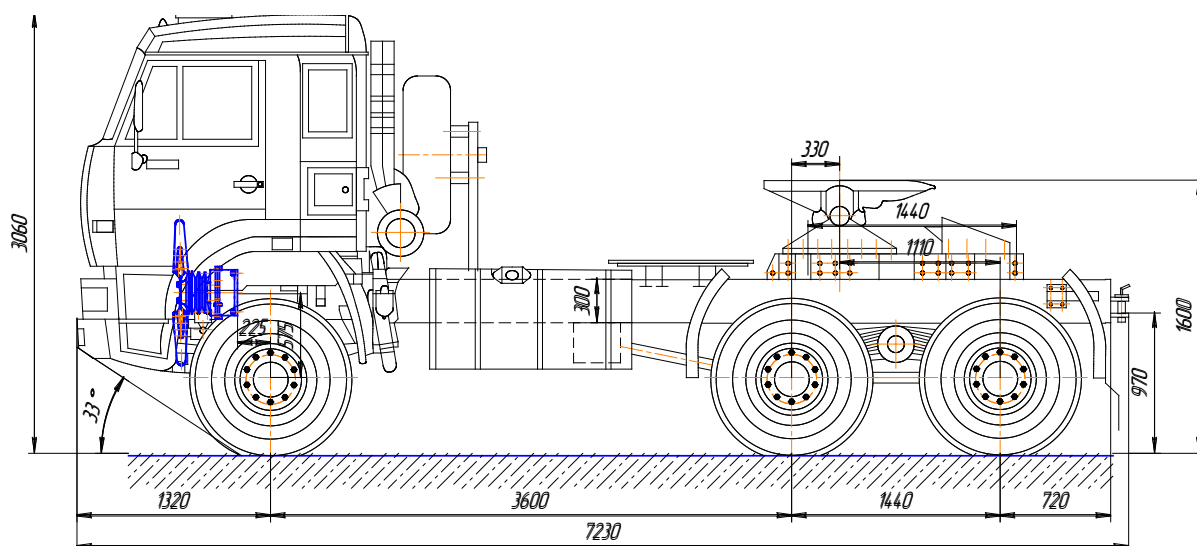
КамАЗ-65225 (колесная формула 6х4) с установленным в передней части двигателя ретардером
